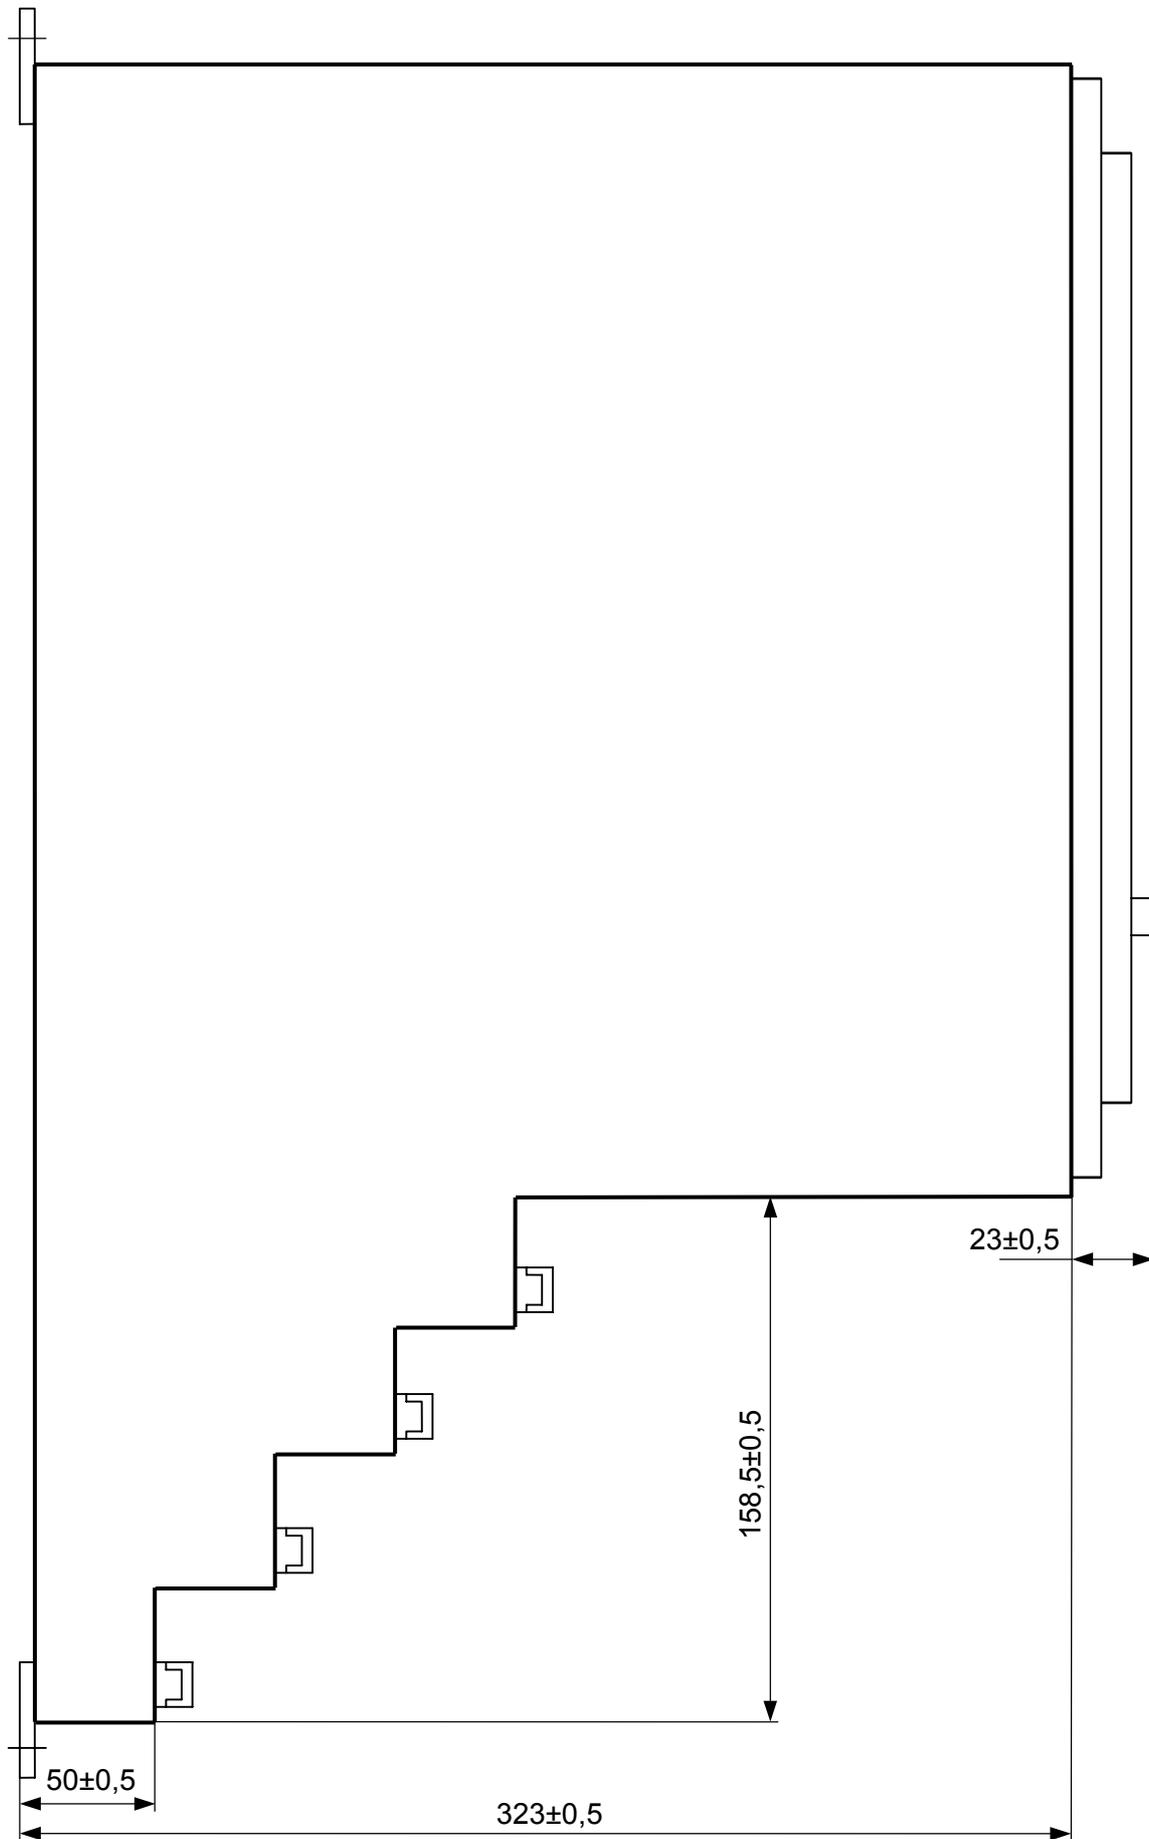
6 Вид сбоку кожуха с установленным МРЗС-05-06
